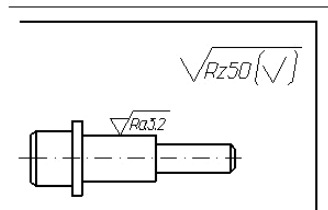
Пример обозначение шероховатости, одинаковой для части поверхностей изделия
